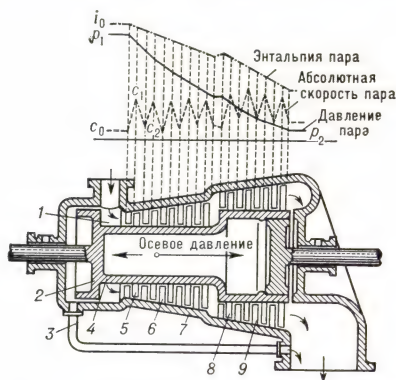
Схематический разрез небольшой реактивной турбины: 1 — кольцевая камера свежего пара; 2 — разгрузочный поршень; 3 — соединительный паропровод; 4 — барабан ротора; 5, 8 — рабочие лопатки; 6, 9 — направляющие лопатки; 7 — корпус.
